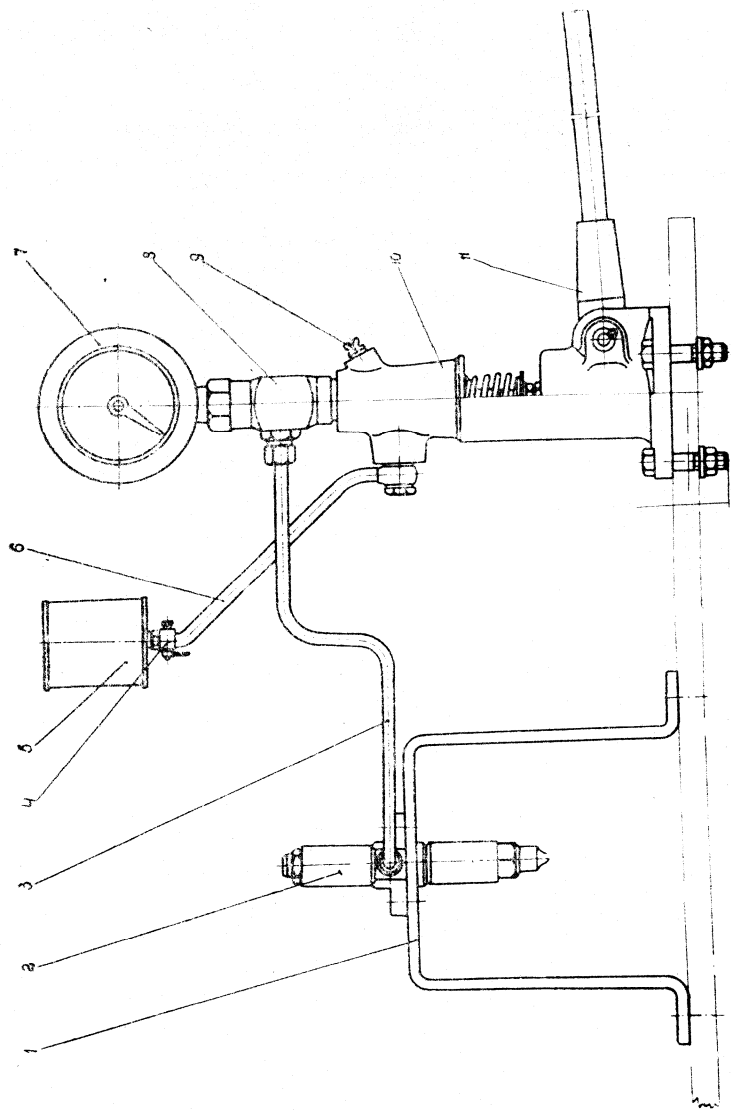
Схема установки приспособления для проверки форсунок: 1 — стойка; 2 — проверяемая форсунка; 3 — нагреваемая трубка; 4 — краник; 5 — бак; 6 — трубка подвода топлива; 7 — манометр; 8 — тройник; 9 — винт для выпуска воздуха; 10 — приспособление для проверки форсунок; 11 — рычаг.
